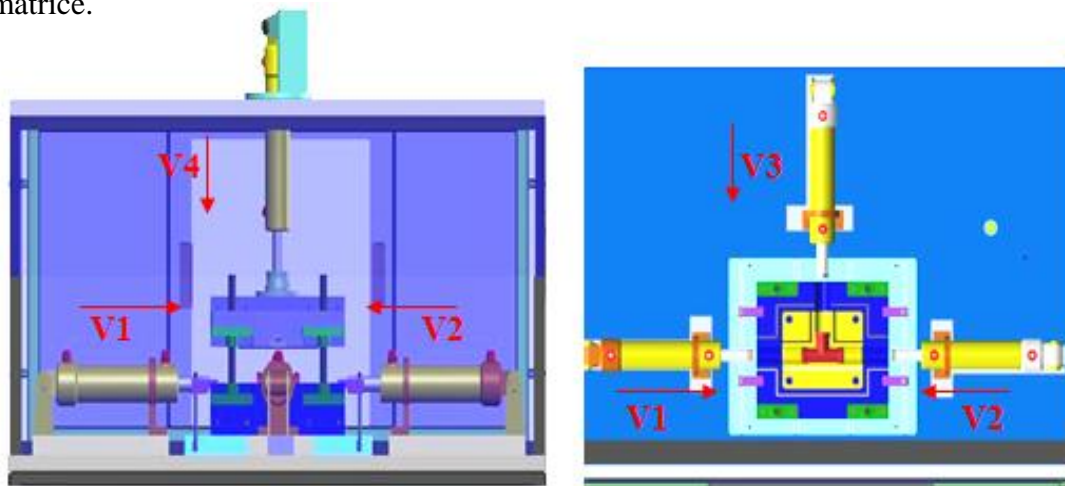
Schéma d'un dispositif de fabrication de tube forme T par procédé hydroformage
